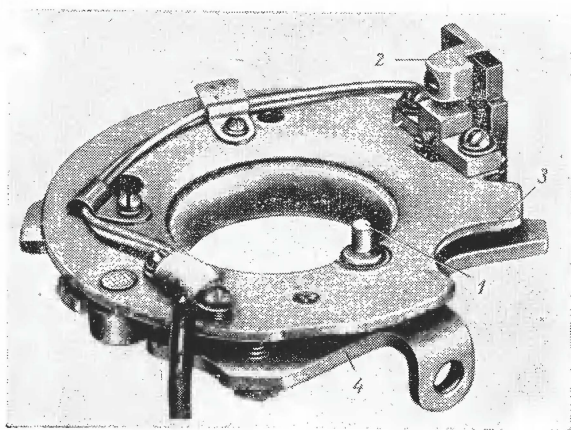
Подвижной диск прерывателя с установленным на нем корпусом фотодиодного датчика.
